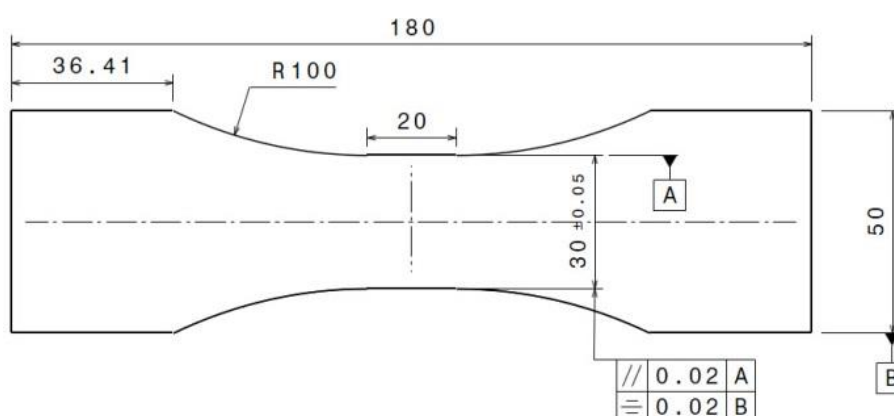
Géométrie lisse des éprouvettes de fatigue
